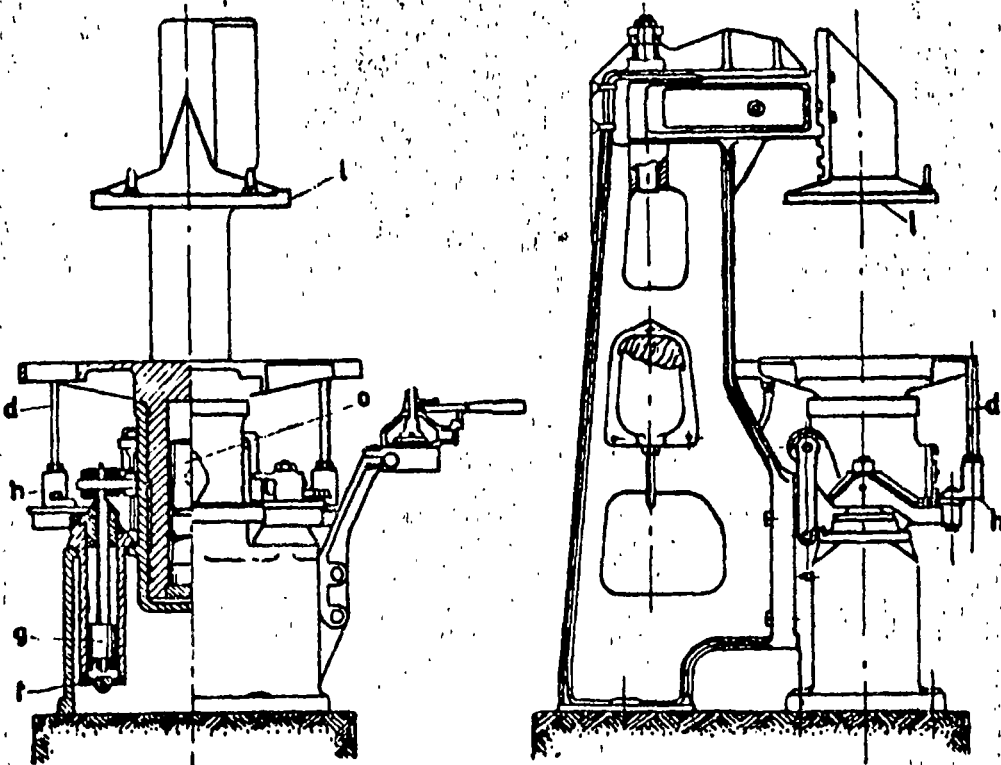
Máquina de moldear por vibrocompresión y de desmoldar. Obsérvense las espigas d para el levantamiento de la caja soportadas por los brazos h regulados por los pistones g, que se deslizan en los cilindros f; e es la masa vibradora, l es el plato de la compresión, giratorio sobre el eje vertical de la máquina.
